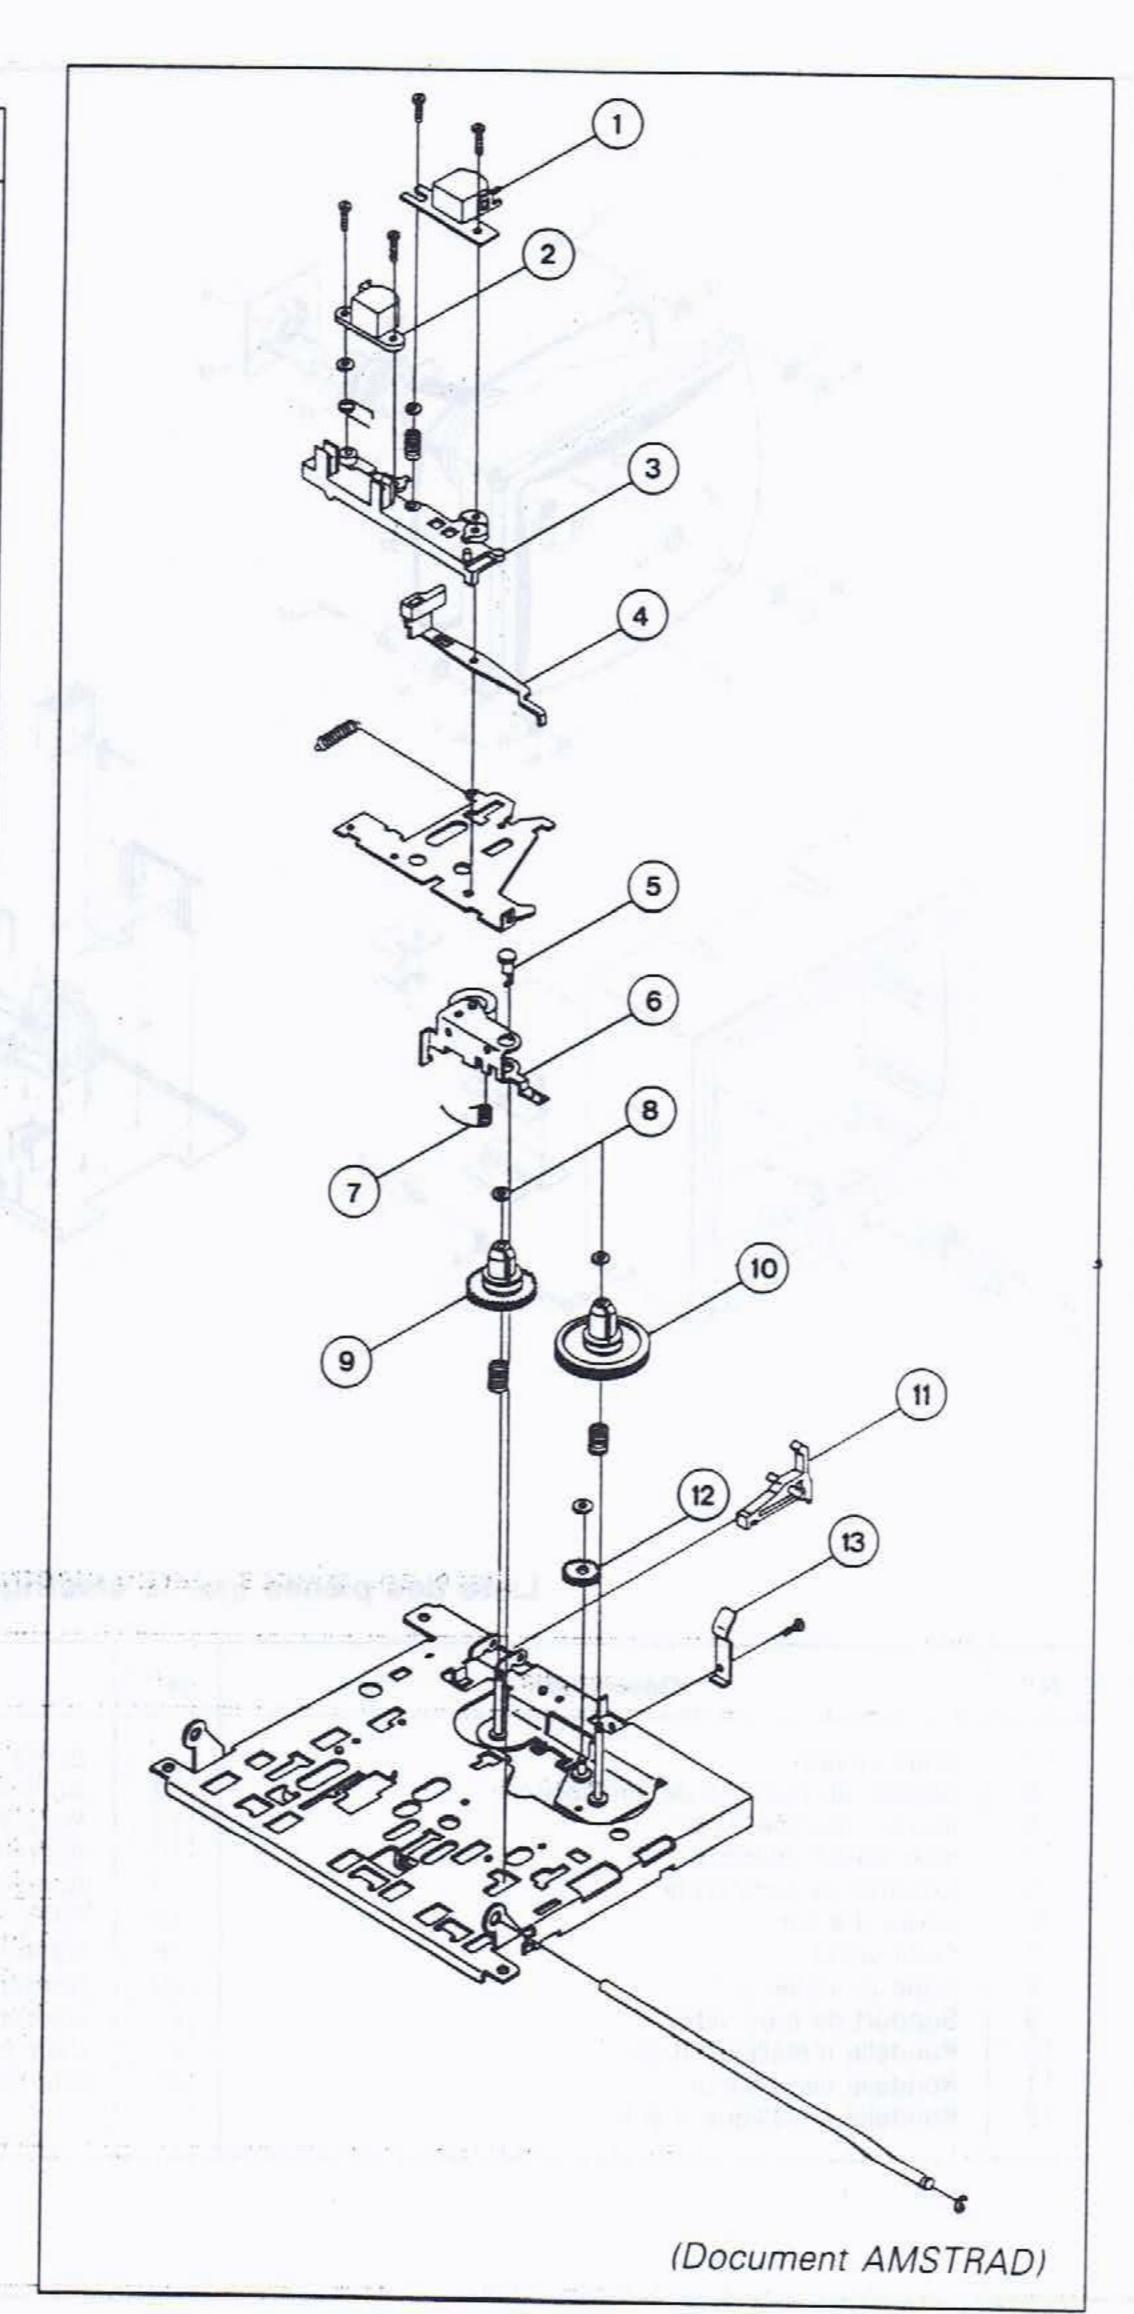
Eclaté mécanique de la platine cassette (dessus).
